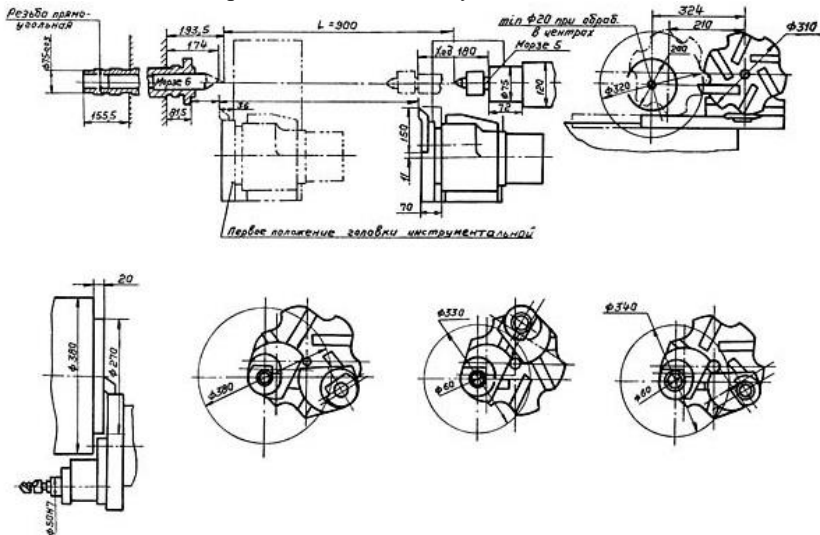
Рабочей зоны станка 16A20Ф3 с шестипозиционной головкой. Станок относится к нормальным по классу точности, следовательно, пригоден для черновой и чистовой обработки заготовок с достижением точности размеров по 10-му качеству.
